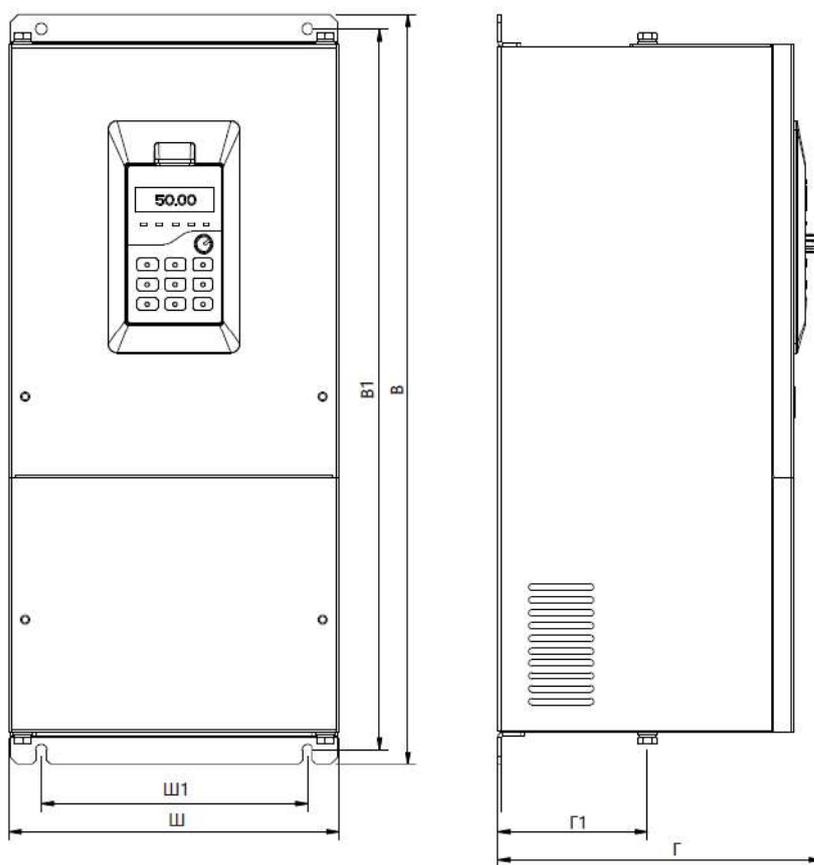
V2000-T0055G и более мощные (металлический корпус)
